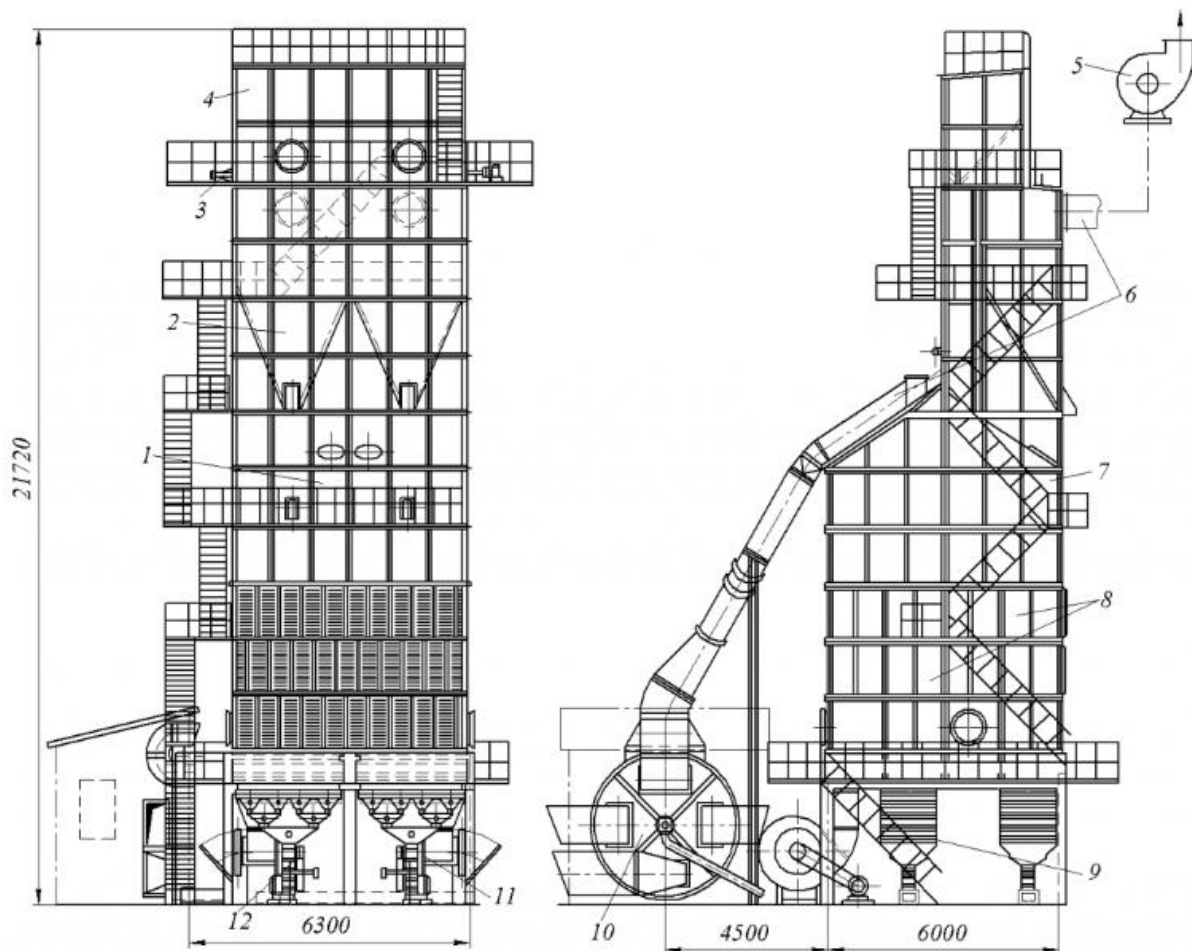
Зерносушильний агрегат РД-2-25-70
